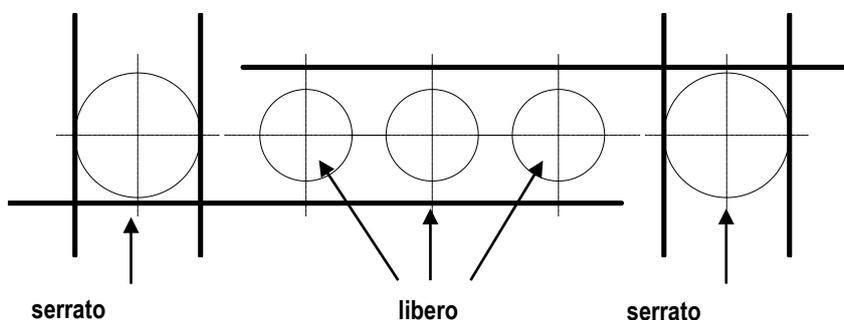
Schema per il premontaggio di un morsetto per cavi tondi
